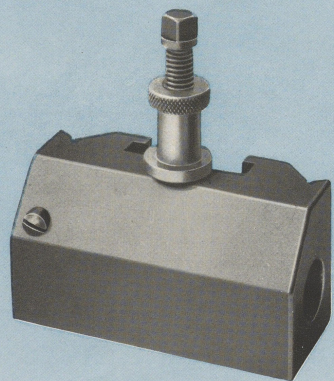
Werkzeughalter mit Morsekonus und Auslösevorrichtung für Spiralbohrer.
